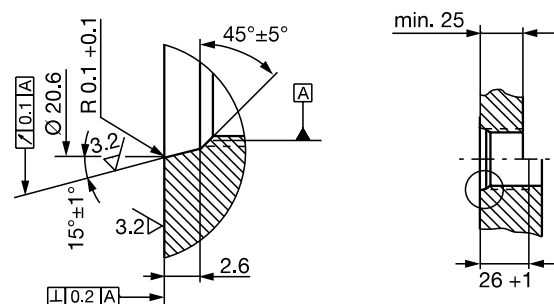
Einschraubloch 3/4"-16UNF nach SAE J475 O-Ring 15.3x2.4
